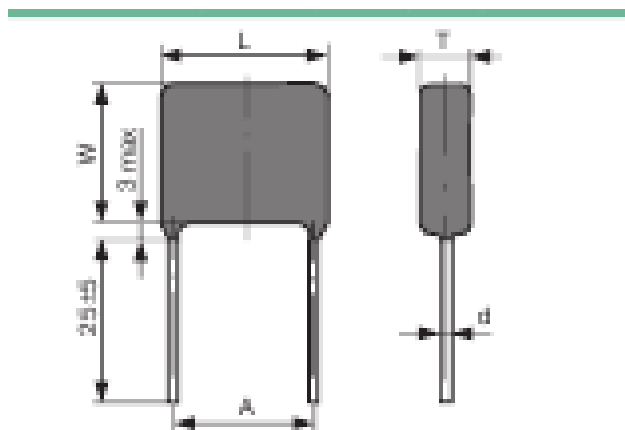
Габарітні розміри конденсатора K73-17
